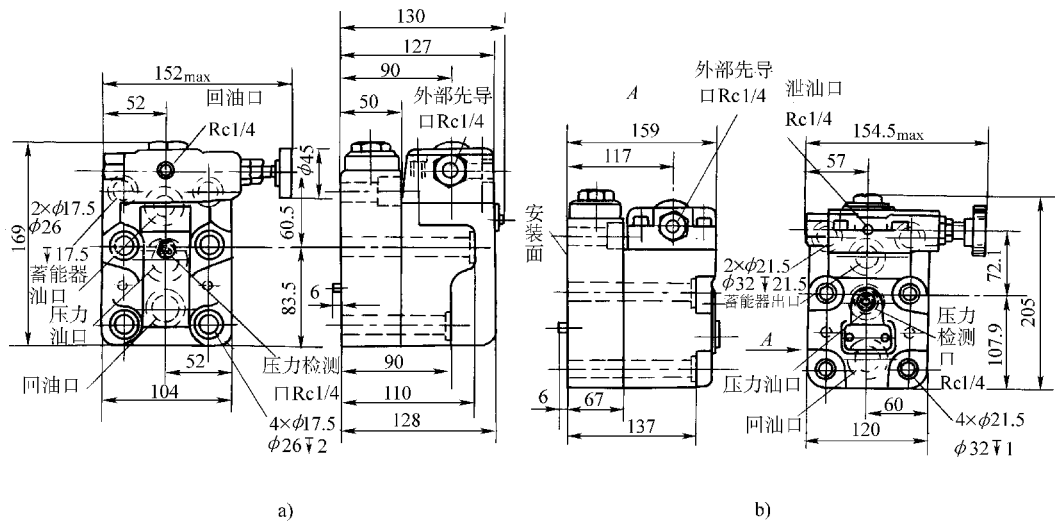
BUC 型卸荷溢流阀外形尺寸
